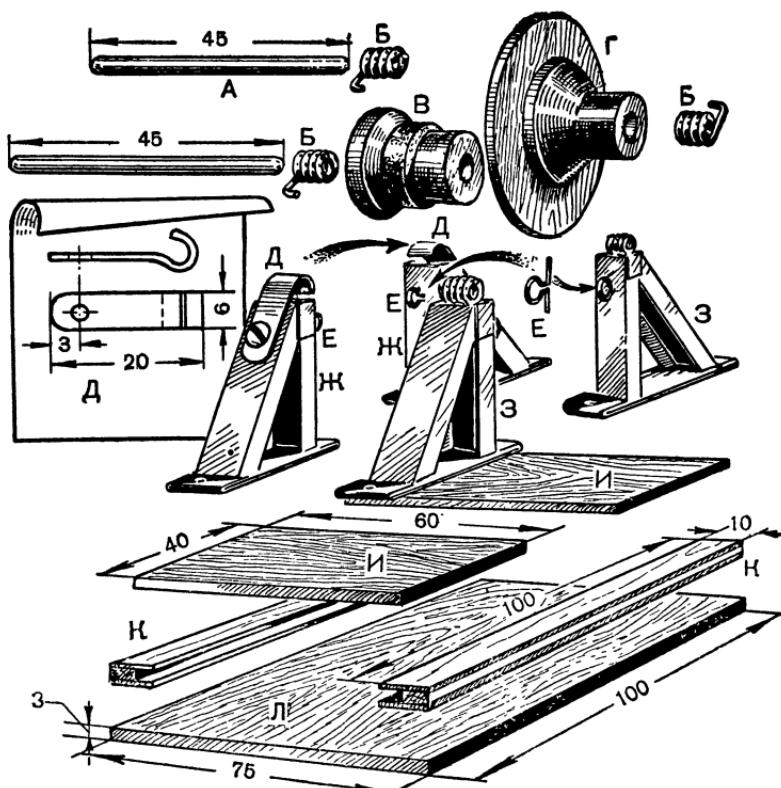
Детали и порядок сборки редукторов №№ 1 и 2: А — валы; Б — подшипники; В — малый фрикцион; Г — большой фрикцион; Д — накладки; Е — петельки для стяжек; Ж — стойки с накладками (для редуктора № 1); З — стойки с подшипниками (для редуктора № 2); И — площадки; К — направляющие; Л — основание.
